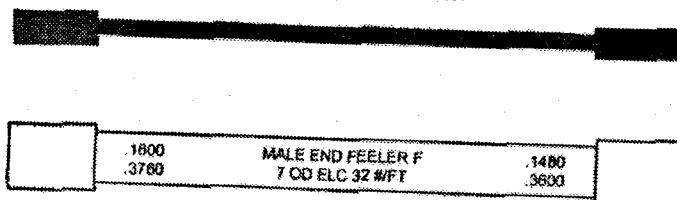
Калибр-пробка для резьбы безмуфтового соединения со скользящим кольцом контроля уплотнения
